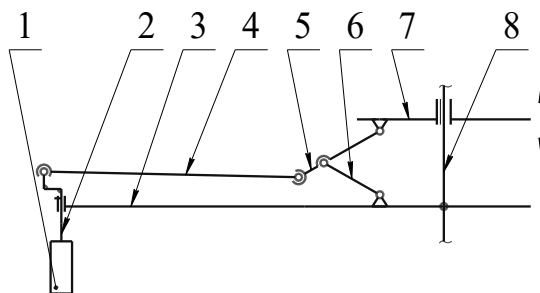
Кінематична схема керованого робочого органа роторного змішувача з механізмом керування важільного типу:
